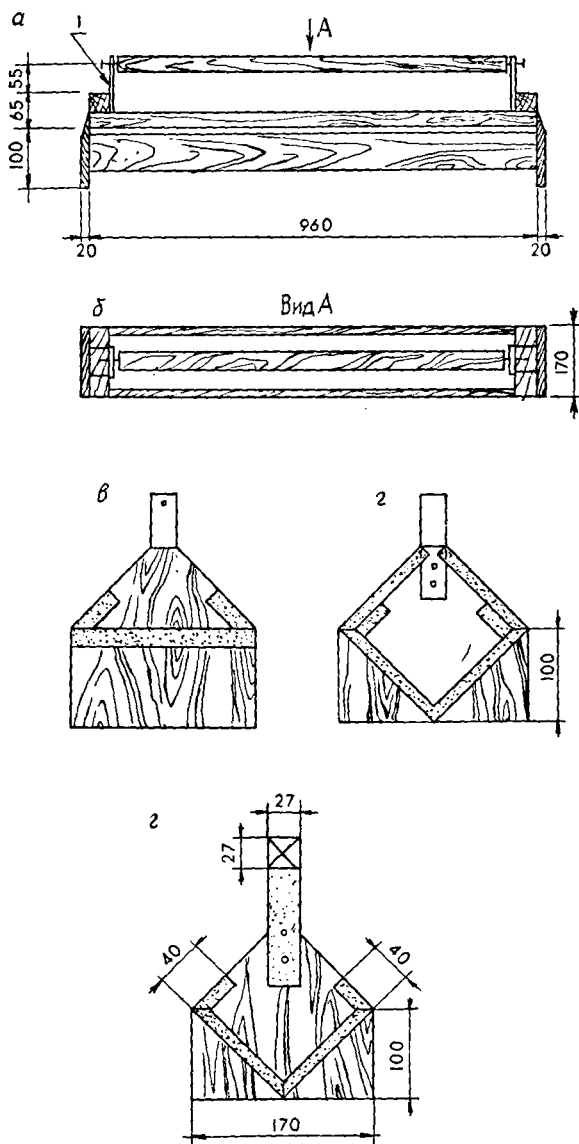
Кормушка для цыплят, индюшат и цесарят:
